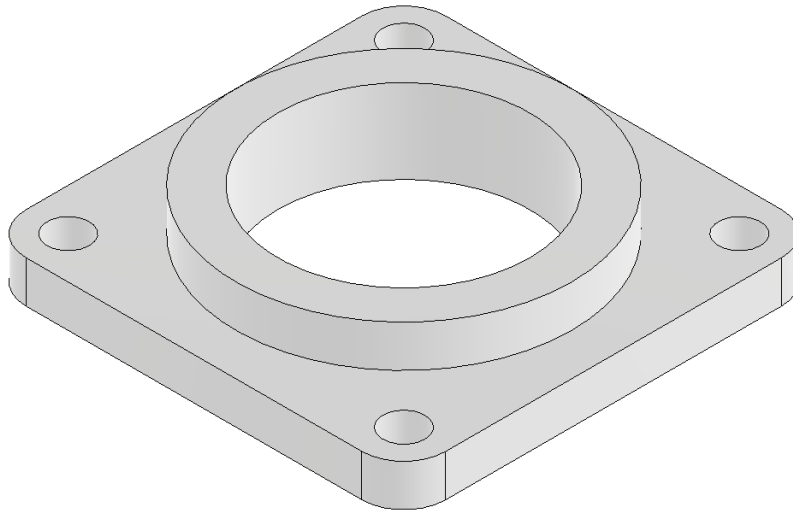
Деталь для обработки на разобленном верстаті
